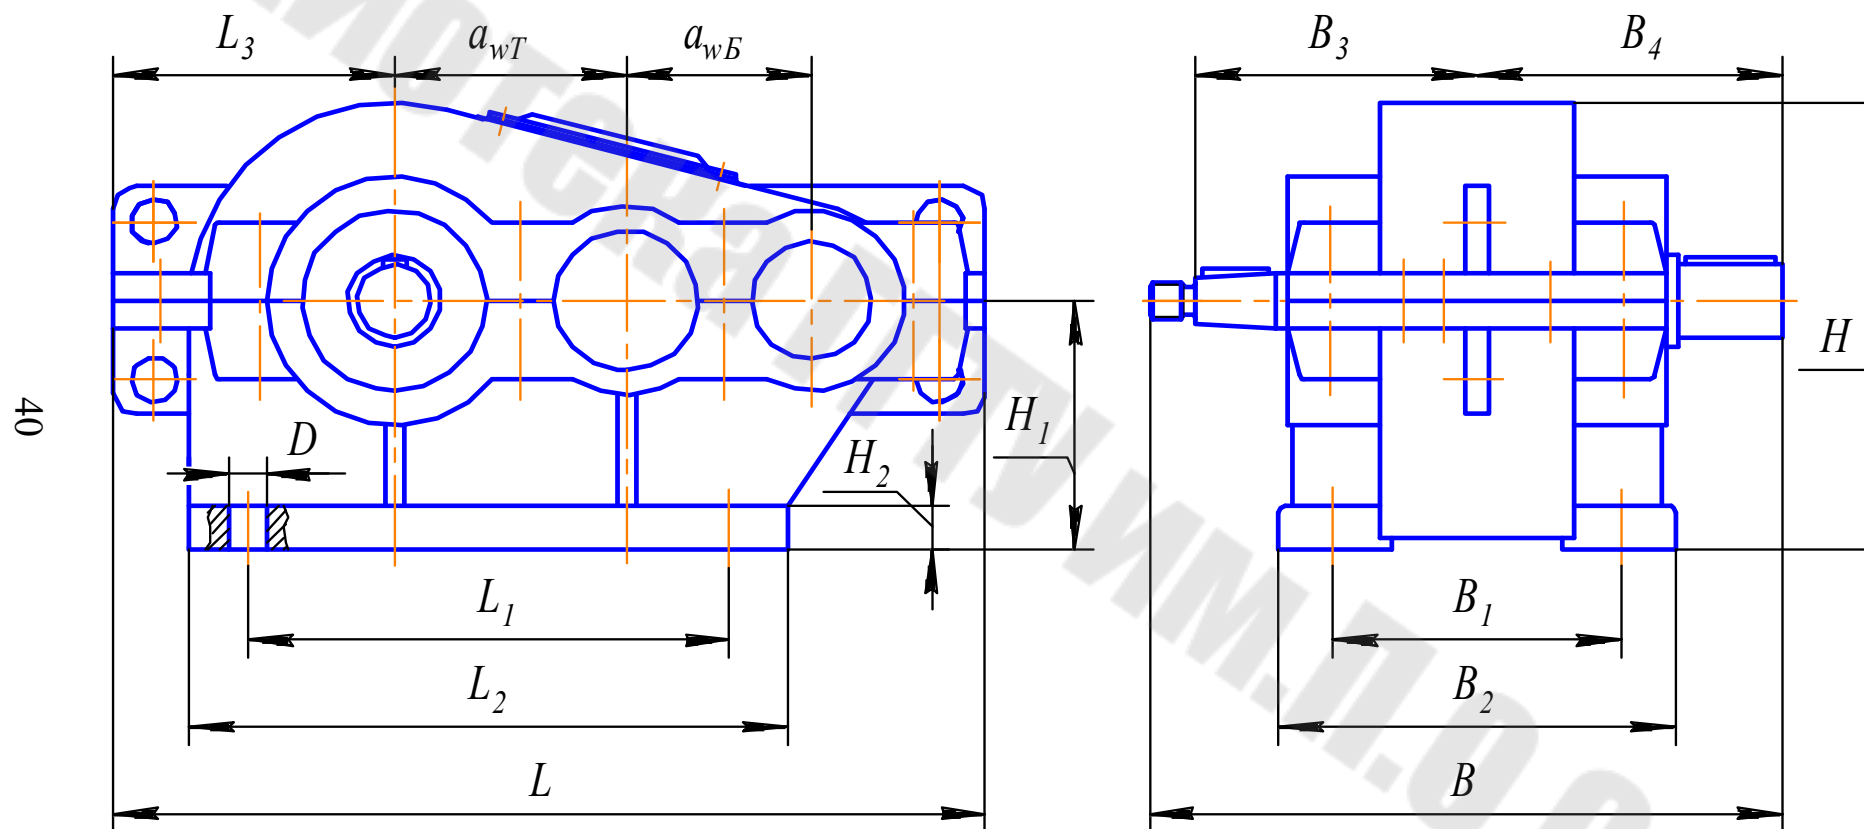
Габаритные и присоединительные размеры цилиндрического редуктора
